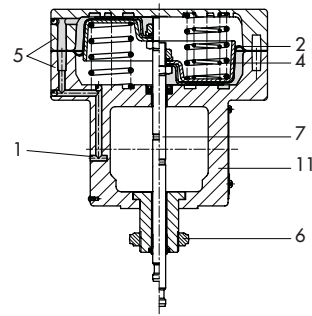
· Tipo 3277-5 para montaje directo de accesorios
